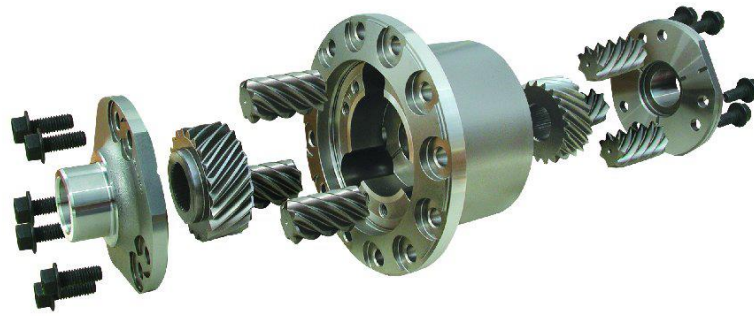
Vista explodida de diferencial do tipo TorSen [16]
